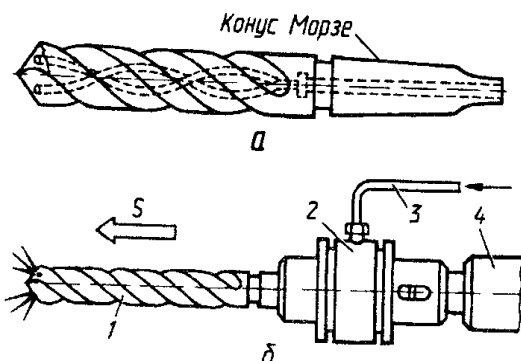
Свердло з внутрішніми каналами підведення охолодної рідини: а - загальний вигляд; б - схема кріплення свердла у спеціальному патроні; 1 - свердло; 2 - патрон; 3 - шланг для підведення МОР; 4 - піноль задньої бабки
